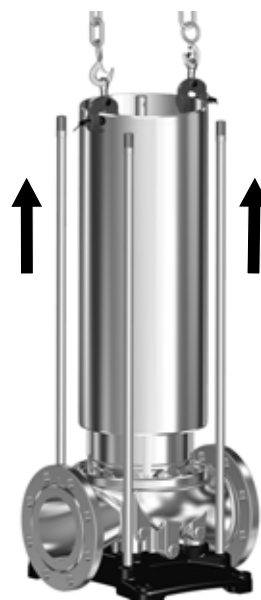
Приспособление N, установленное на цилиндрическом кожухе (55)
